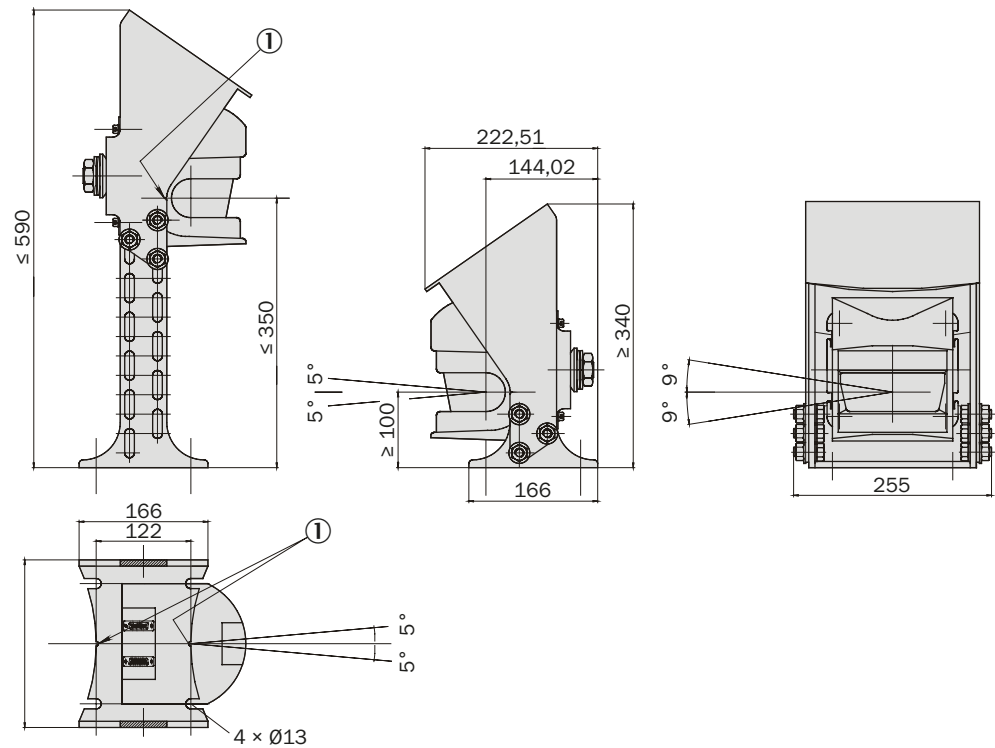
Plan côté kit de fixation charge élevée (mm)
